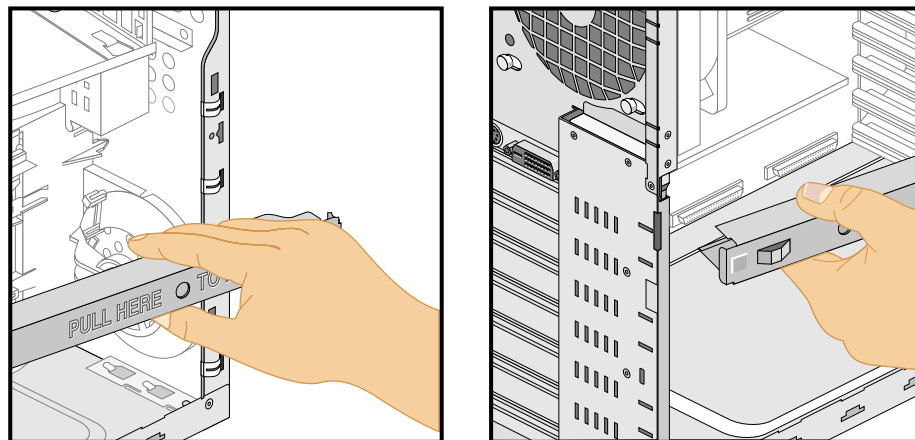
Wegschwenken des Bügels vom Gehäuse
